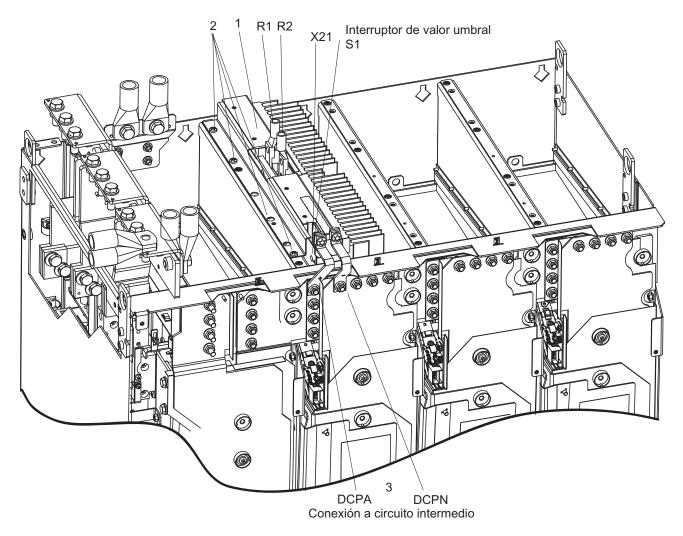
Montaje del Braking Module en un Power Module de tamaño JX
